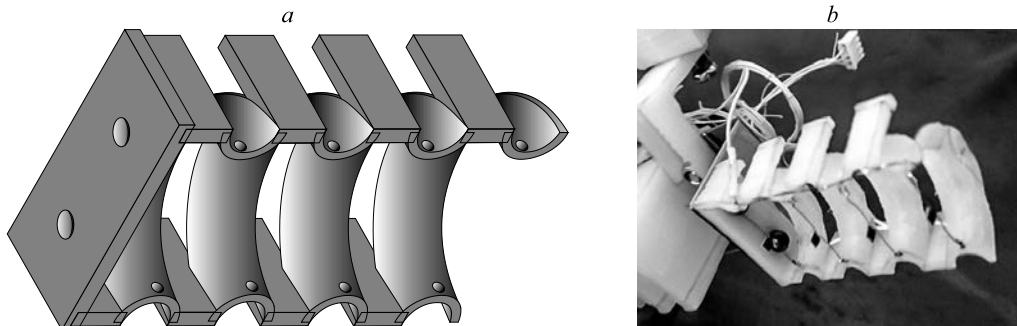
Трехмерная модель блока защитных козырьков (a) и фотография готового образца (b).
